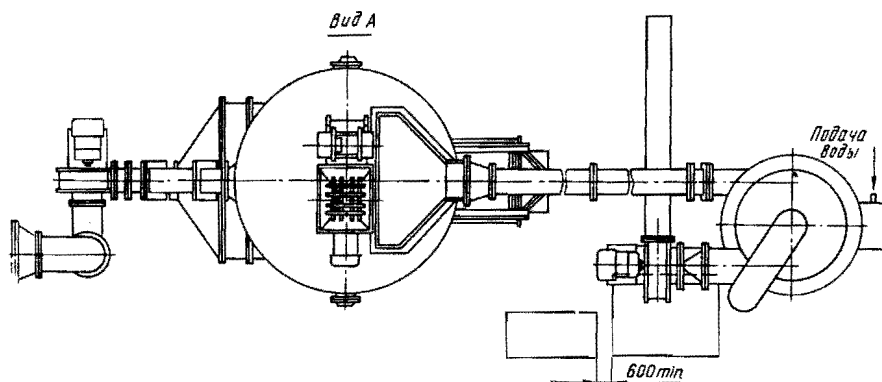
Общий вид установки марки РЗ-ОСС для сушки молочного сахара:
